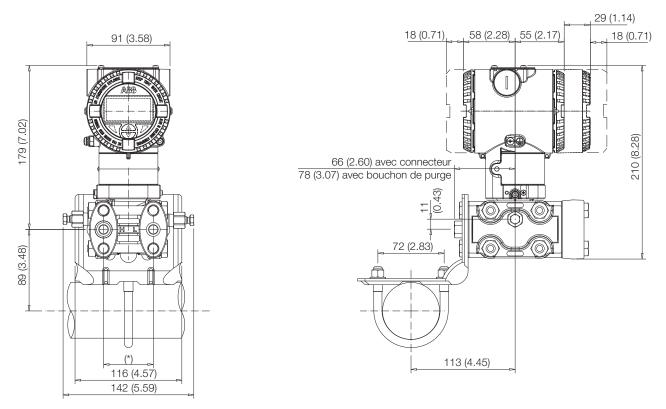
Transmetteur de pression différentielle équipé d'un boîtier de type barillet installé sur un tuyau horizontal avec support de montage en option (B2)
